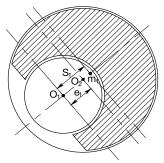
К уравновешиванию центра масс кольца 1 шипника
